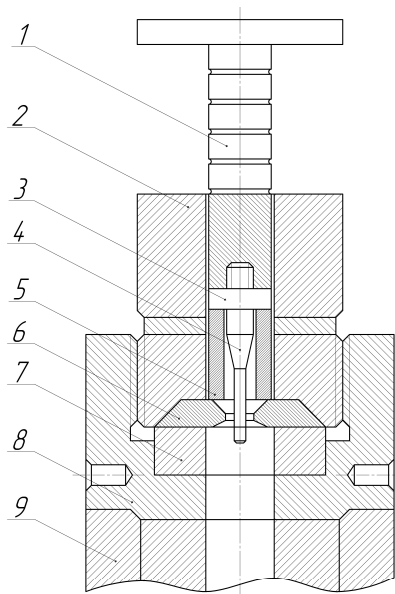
Комплекс прессового инструмента для физического моделирования процесса прессования: 1 – пуансон; 2 – контейнер; 3 – пресс-шайба; 4 – пресс-игла; 5 – заготовка; 6 – матрица; 7 – упор матрицы; 8 – упор контейнера; 9 – удлинитель
